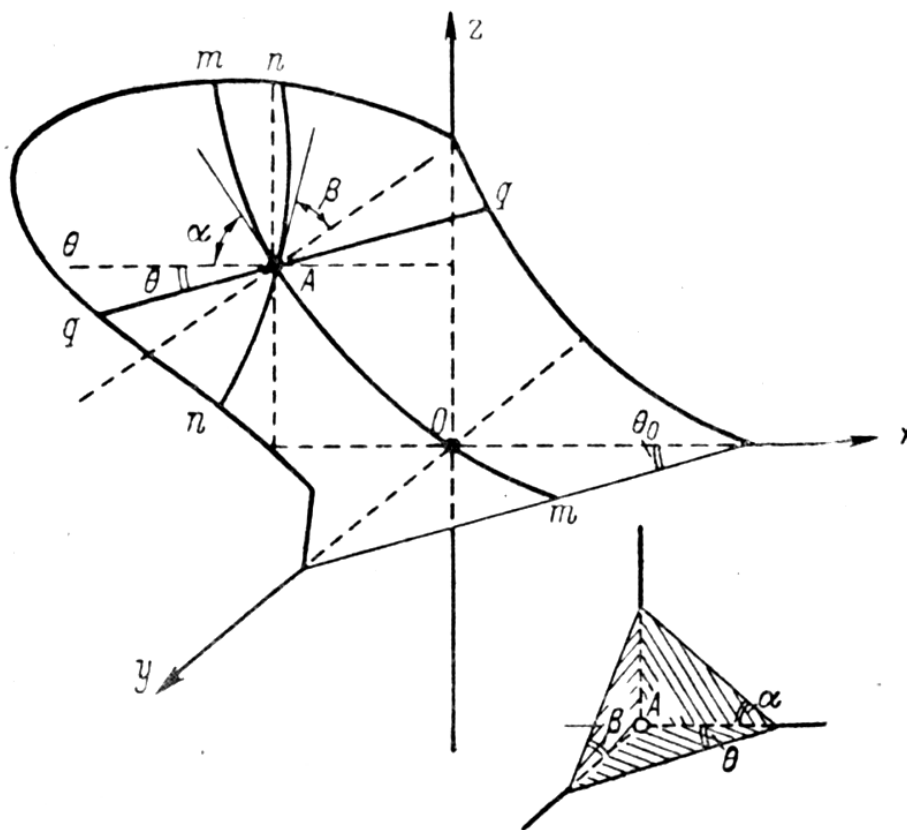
Елементарний тригранний клин і його розвиток у робочу поверхню корпусу плуга.
